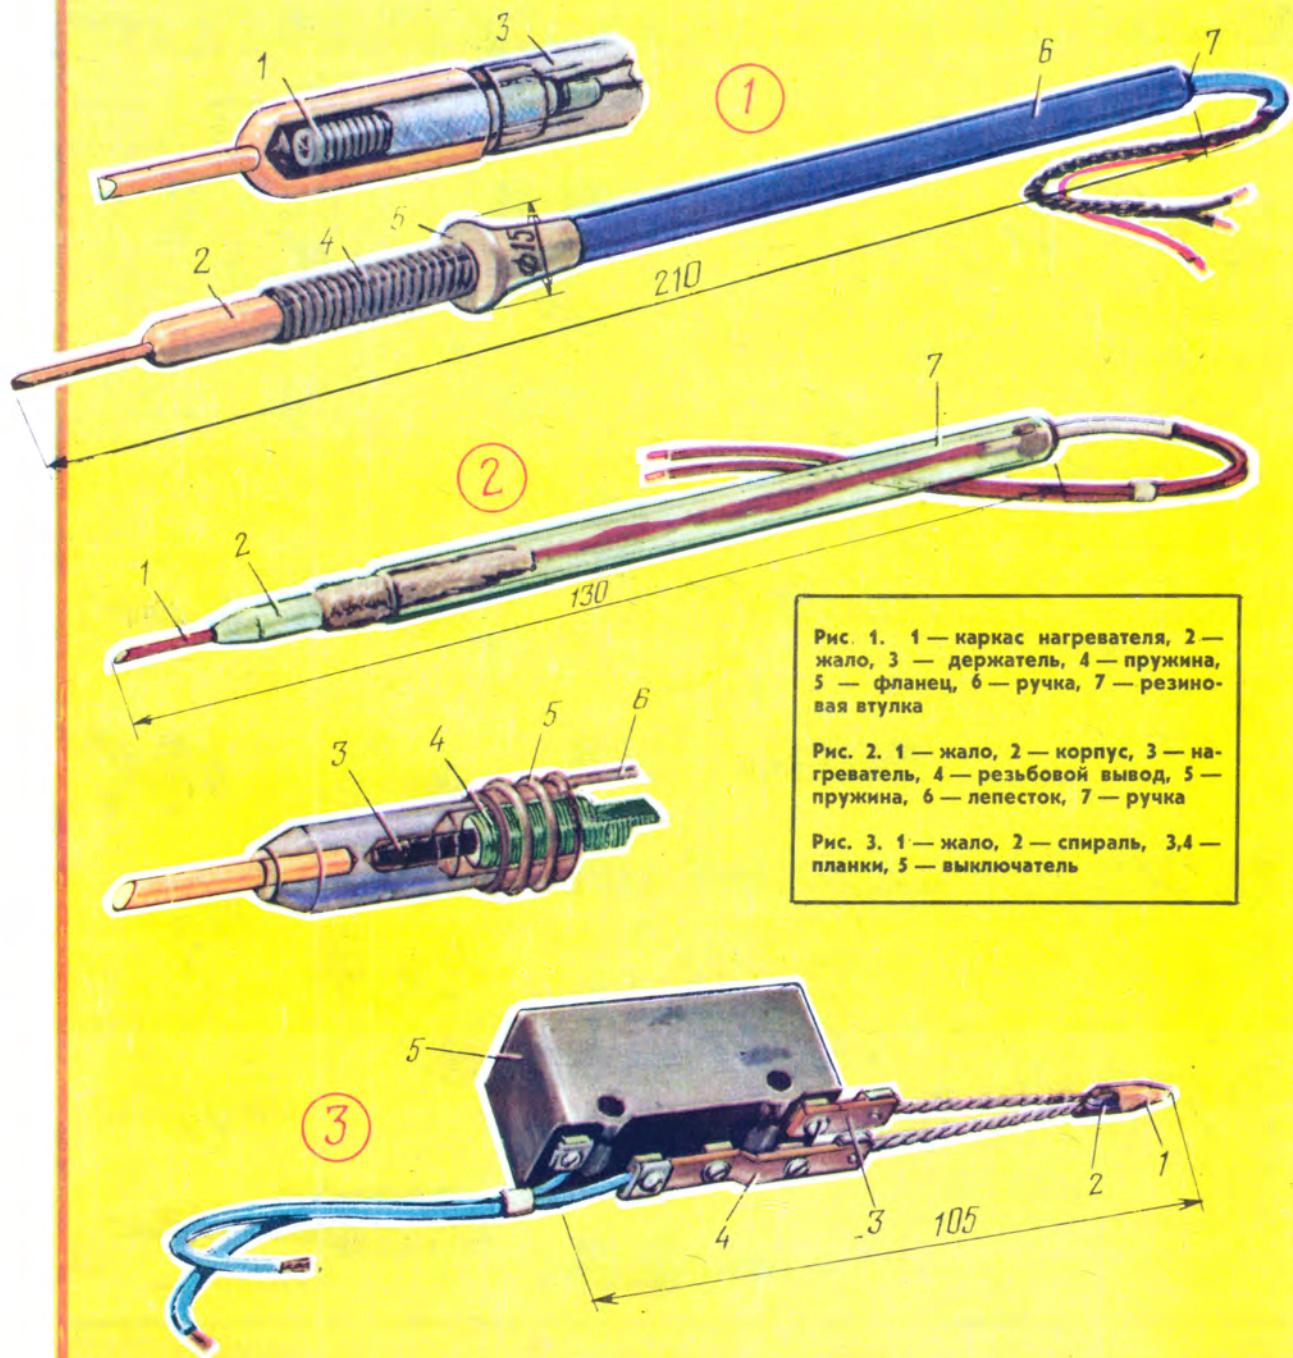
1 — каркас нагревателя, 2 — жало, 3 — держатель, 4 — пружина, 5 — фланец, 6 — ручка, 7 — резиновая втулка
